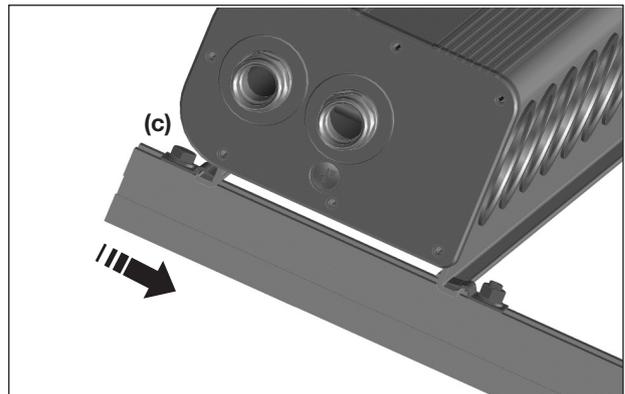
Déplacer la plaque de serrage (c) vers le «bas». Serrer à fond les deux vis M8.
